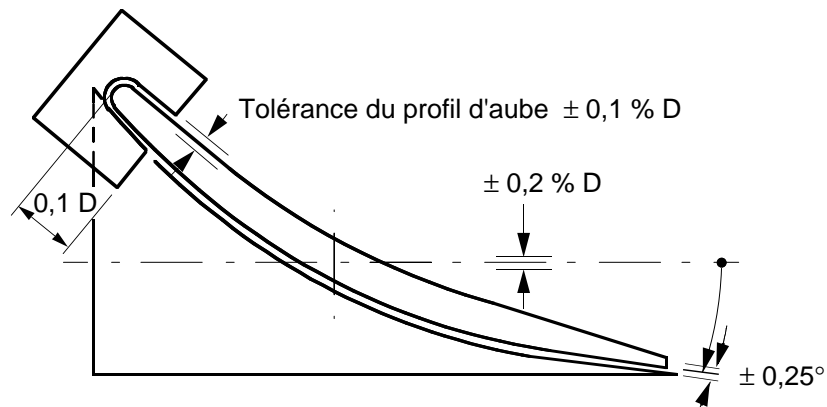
Roue de machine axiale. Définition de l'ajustement des pales et de la tolérance sur leur profil
